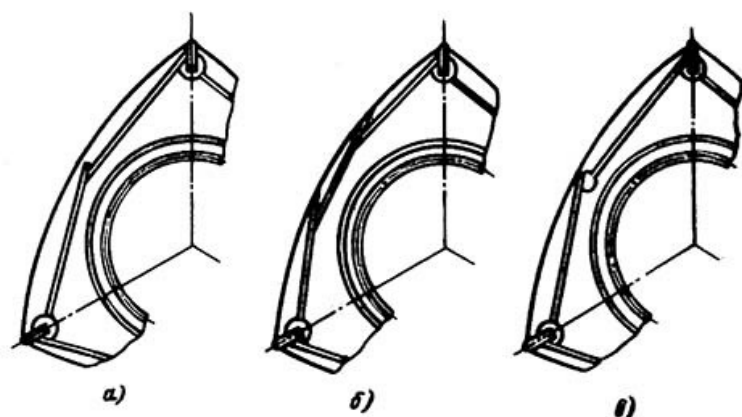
Конструкции роторов с прямолинейными торцовыми пластинами
